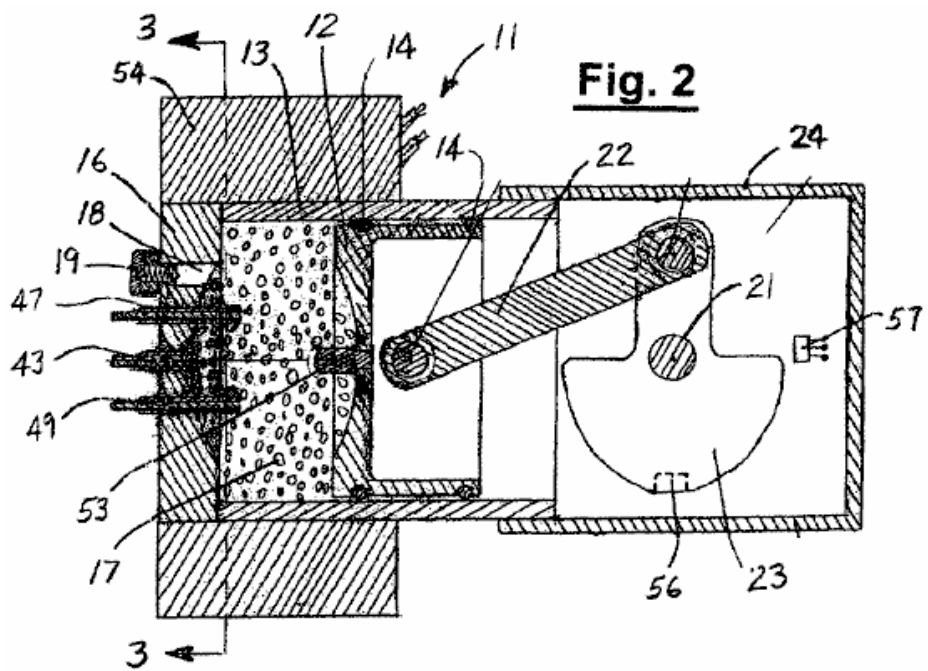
è una vista in sezione, presa lungo la linea 2-2 nella Fig.1.
